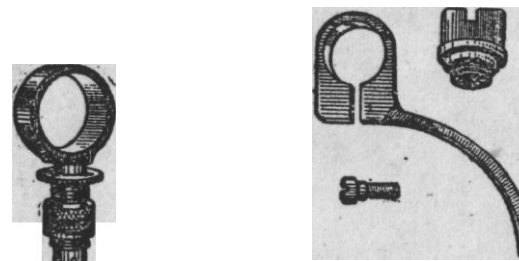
Детали установочного приспособления для прикрепления малокалиберного пулемет» к пулемету Максима
